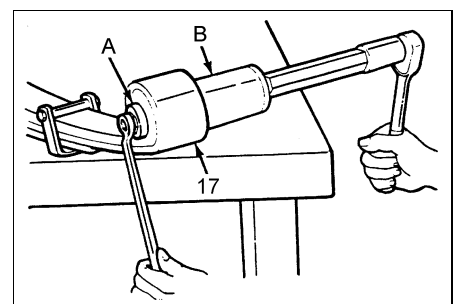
Установка втулки рессоры. 17 - рессора, А - приспособление для установки и снятия втулок, В - дополнительный упор приспособления.
